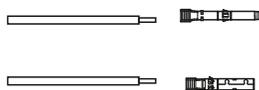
Insertar el cable en la tapa de la tuerca y el pin de contacto
